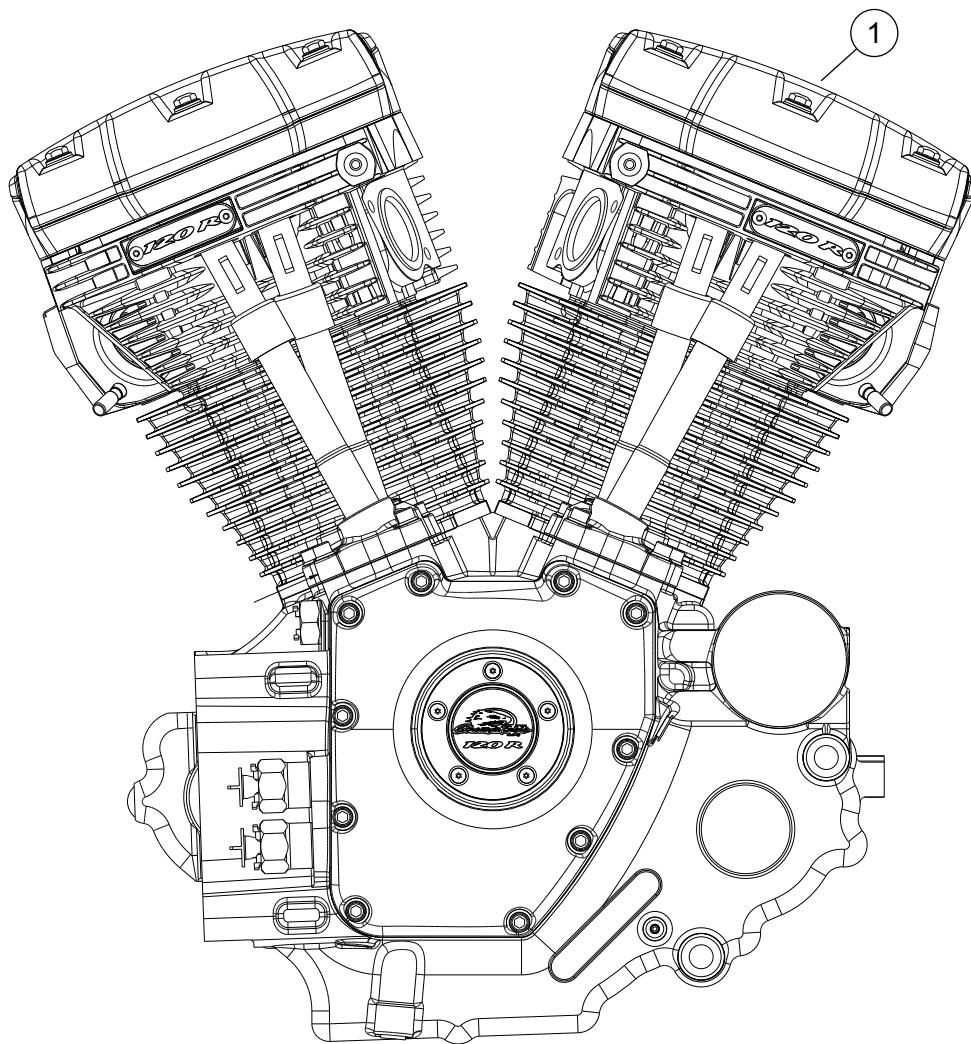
Conjunto del motor, motor ensamblado Screamin' Eagle Pro 120R (Beta) completo
